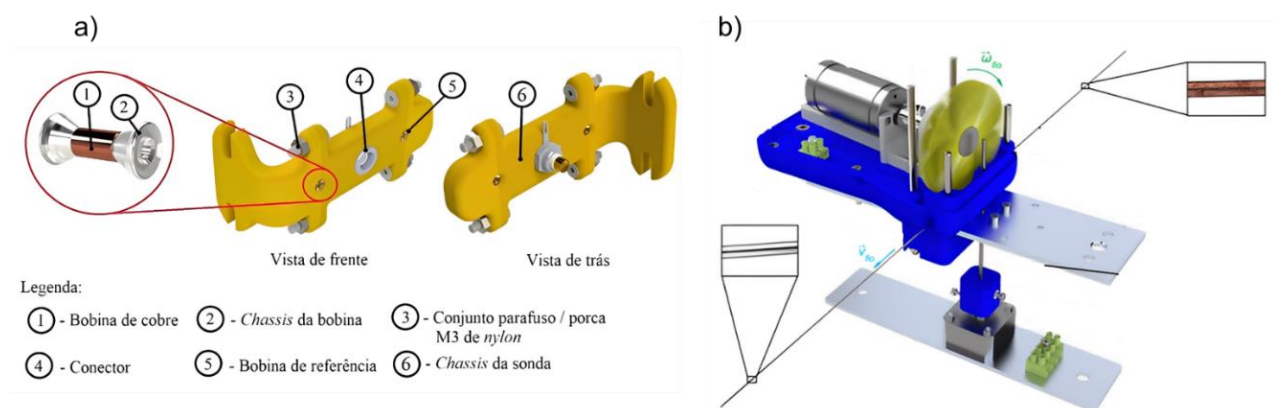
Inspeção e limpeza do fio de soldadura: (a) Sonda de inspeção do fio consumível; [52] (b) EROI V2 [53]
